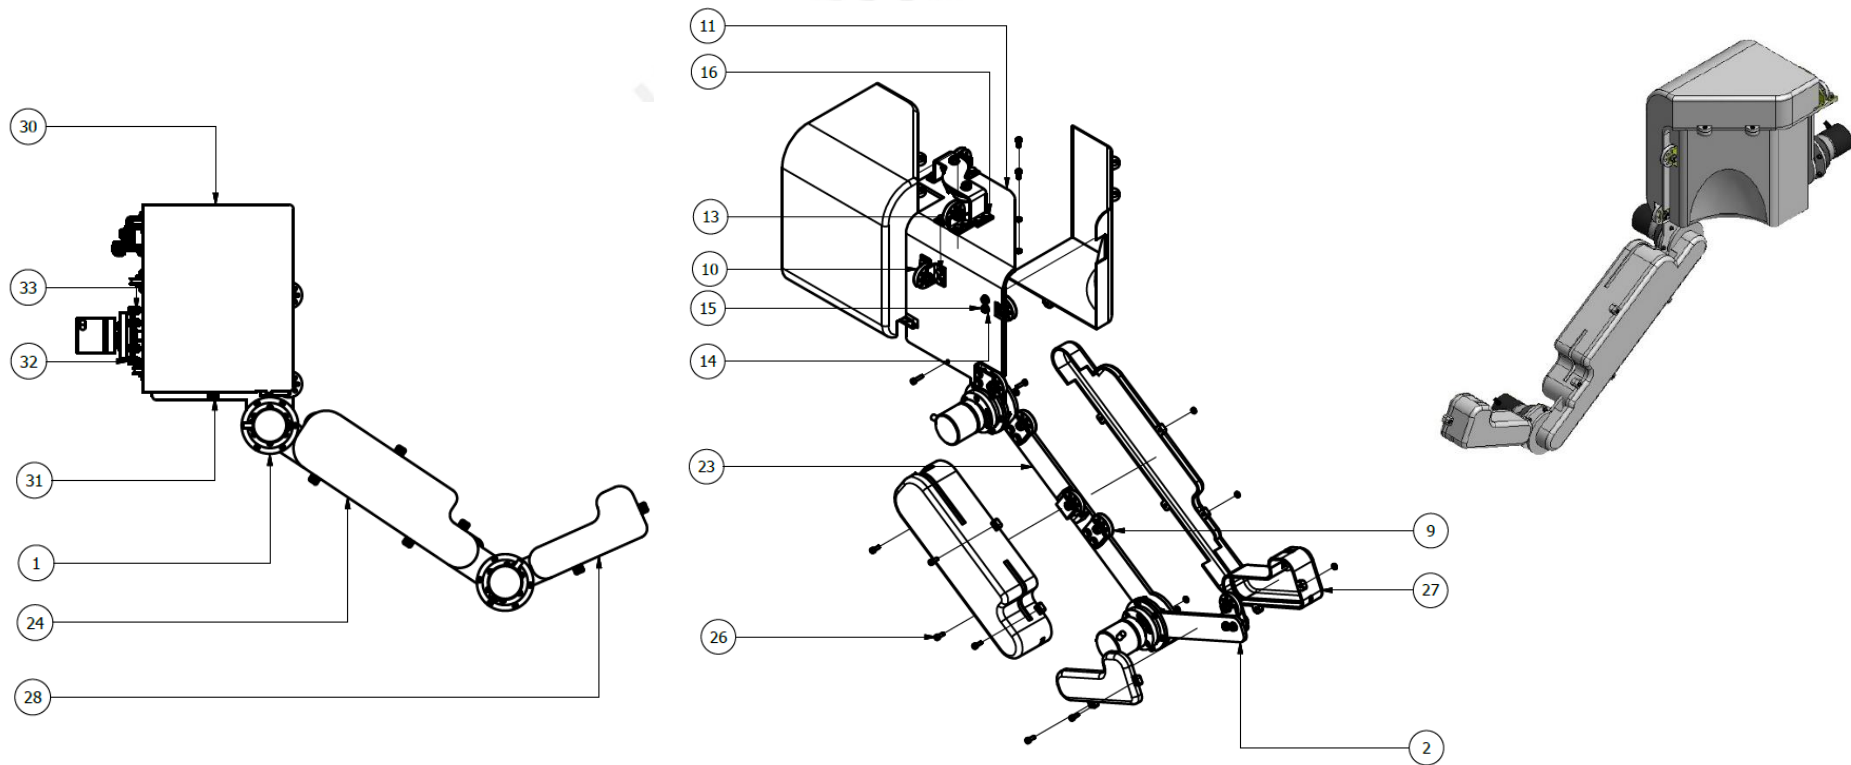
Vistas del plano de ensamble de la parte móvil (primera parte)
